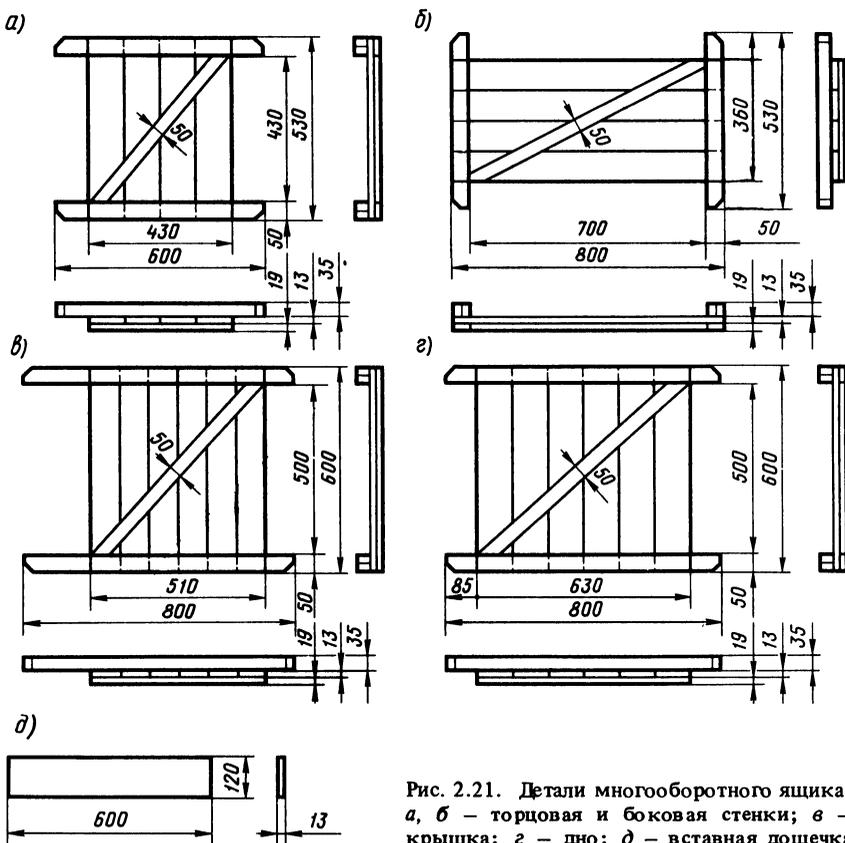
Детали многооборотного ящика: а, б – торцовая и боковая стенки; в – крышка; г – дно; д – вставная дощечка
